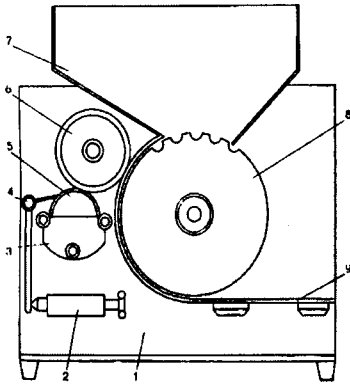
Машина для маркування ампул АП-20М: 1 - корпус; 2 - регулюючий пристрій; 3 - ванна; 4 - ракель; 5 - формовий циліндр; 6 - офсетний циліндр; 7 - бункер; 8 - барабан подачі ампул; 9 - направляючі
